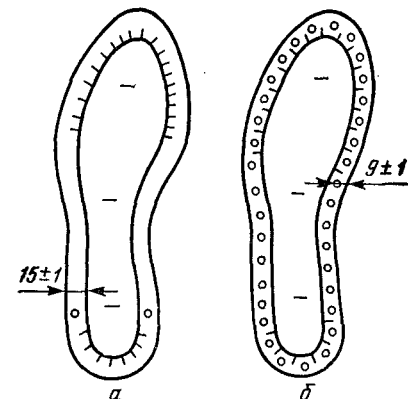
Схемы затяжки геленочной части заготовки верха
